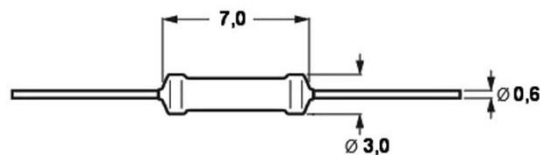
Габаритні розміри конденсатора типу b41828
